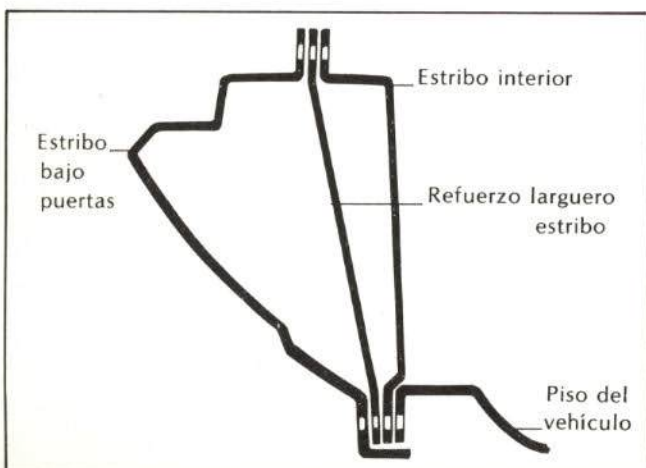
Unión larguero estribo bajo puertas a carrocería.
